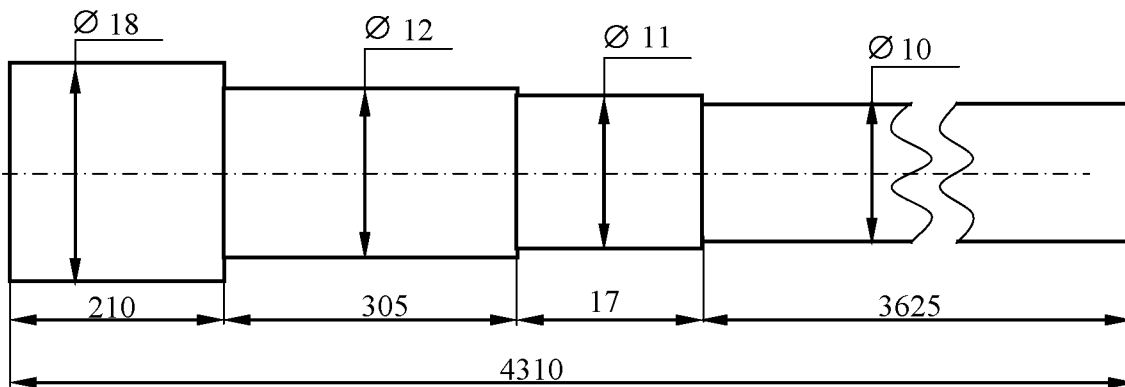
Эскиз ведущего вала привода механизма передвижения рельсовой грузоподъемной машины
